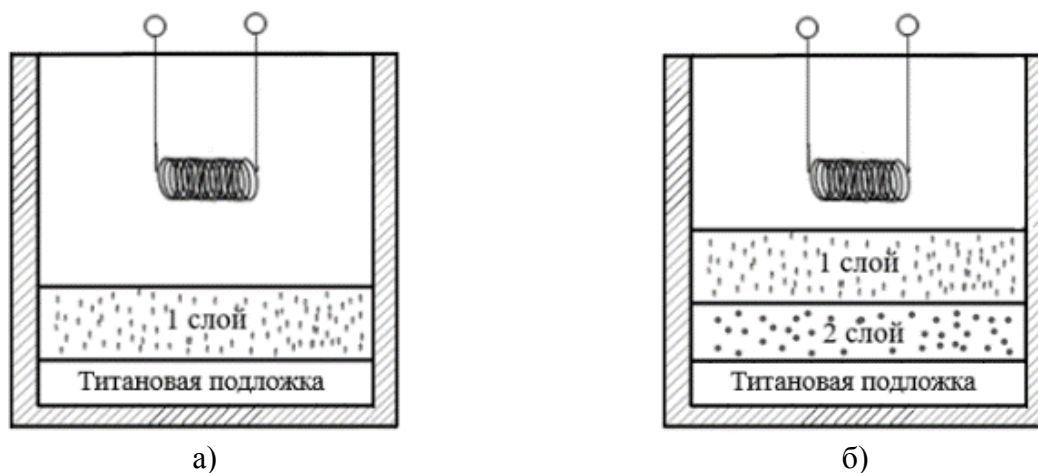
Схемы однослойной и двухслойной наплавки
